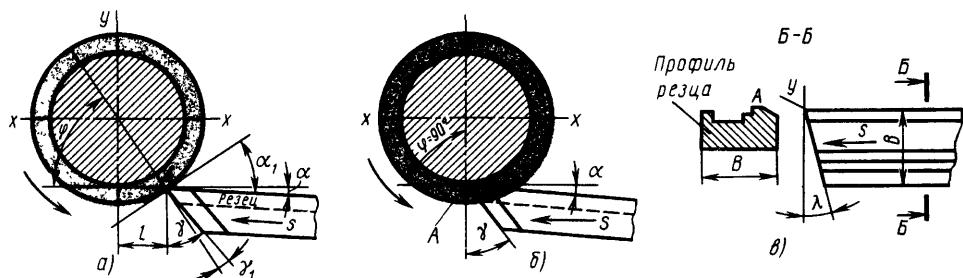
Призматические тангенциальные резцы с режущей кромкой, расположенной перпендикулярно (а и б) и под углом  $\lambda$  (в) к обрабатываемой поверхности
